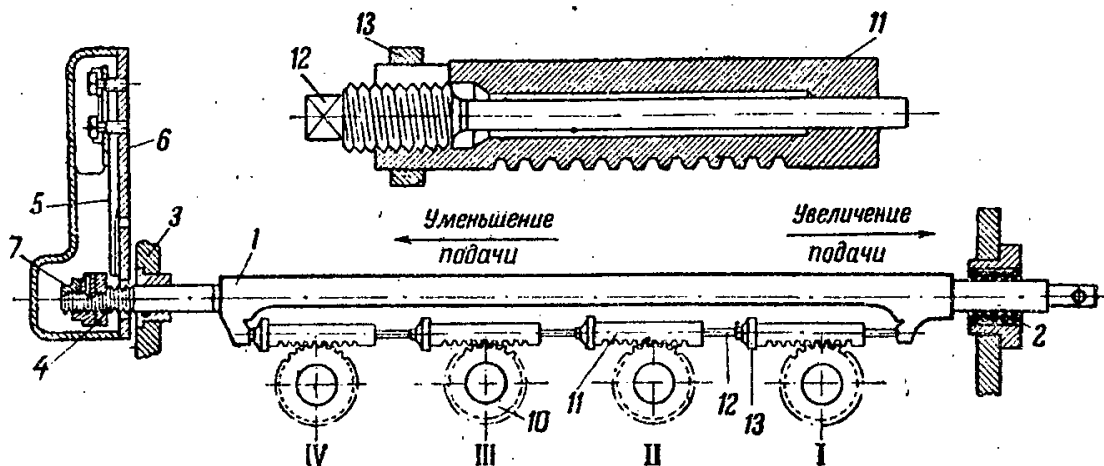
Схема механизма регулирования количества подаваемого топлива: 1 — тяга; 2 и 3 — бронзовые втулки; 4 — фасонная гайка; 5 — плоская пружина; 6 — плита; 7 — угольник; 10 — шестерня поворота плунжера; 11 — рейка; 12 — наконечник; 13 — стопорное кольцо
